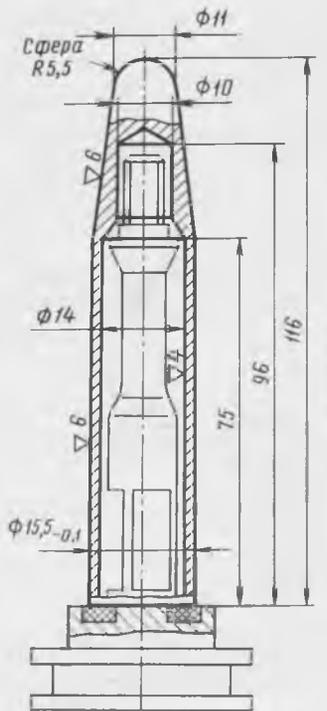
Оправка для установки на поршне клапана нижнего резинового кольца
